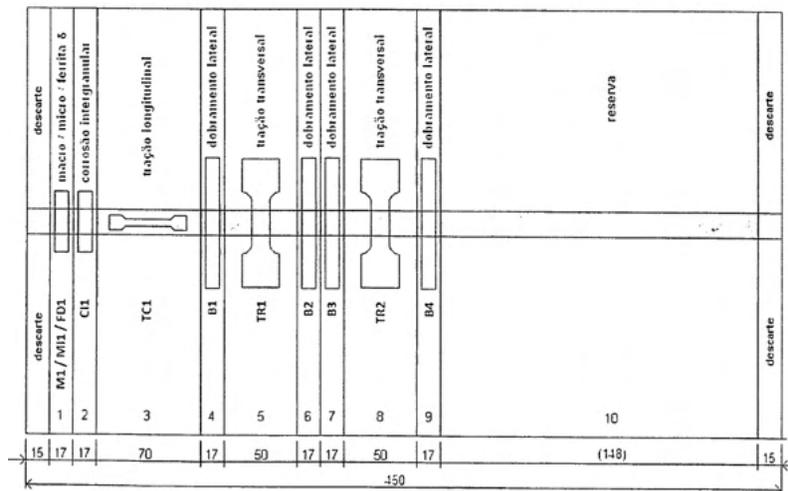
Layout da retirada dos Corpos de Prova (CP's) das amostra (unidades em mm)
